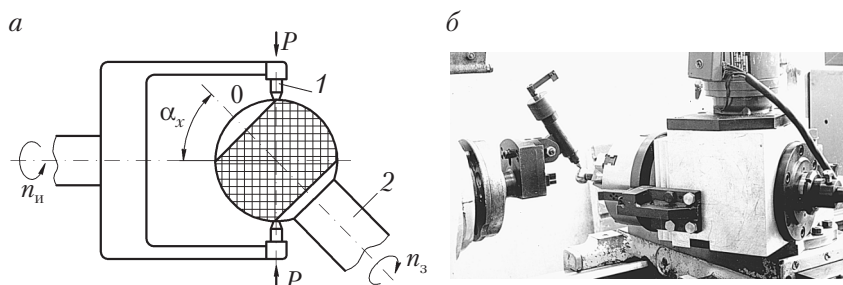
Схема способа образования РМР на сферической поверхности грибка двигателя внутреннего сгорания (а) и алмазное вибровыглаживание грибка на токарно-винторезном станке мод. 1Е61 с помощью специального приспособления (б)
